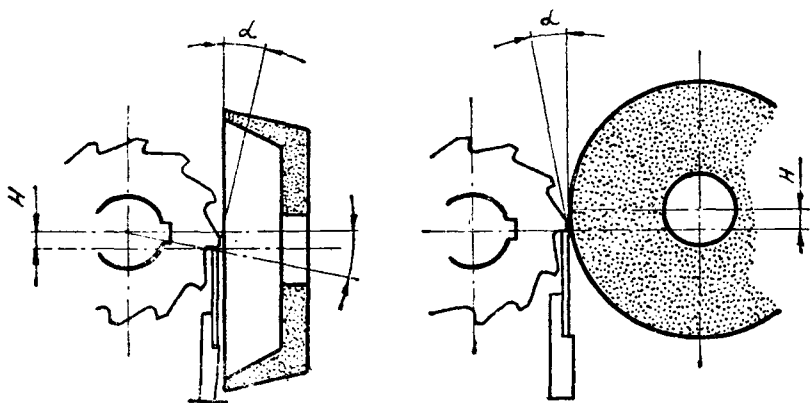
Установка шлифовального круга при заточке фрез с европейским зубом
